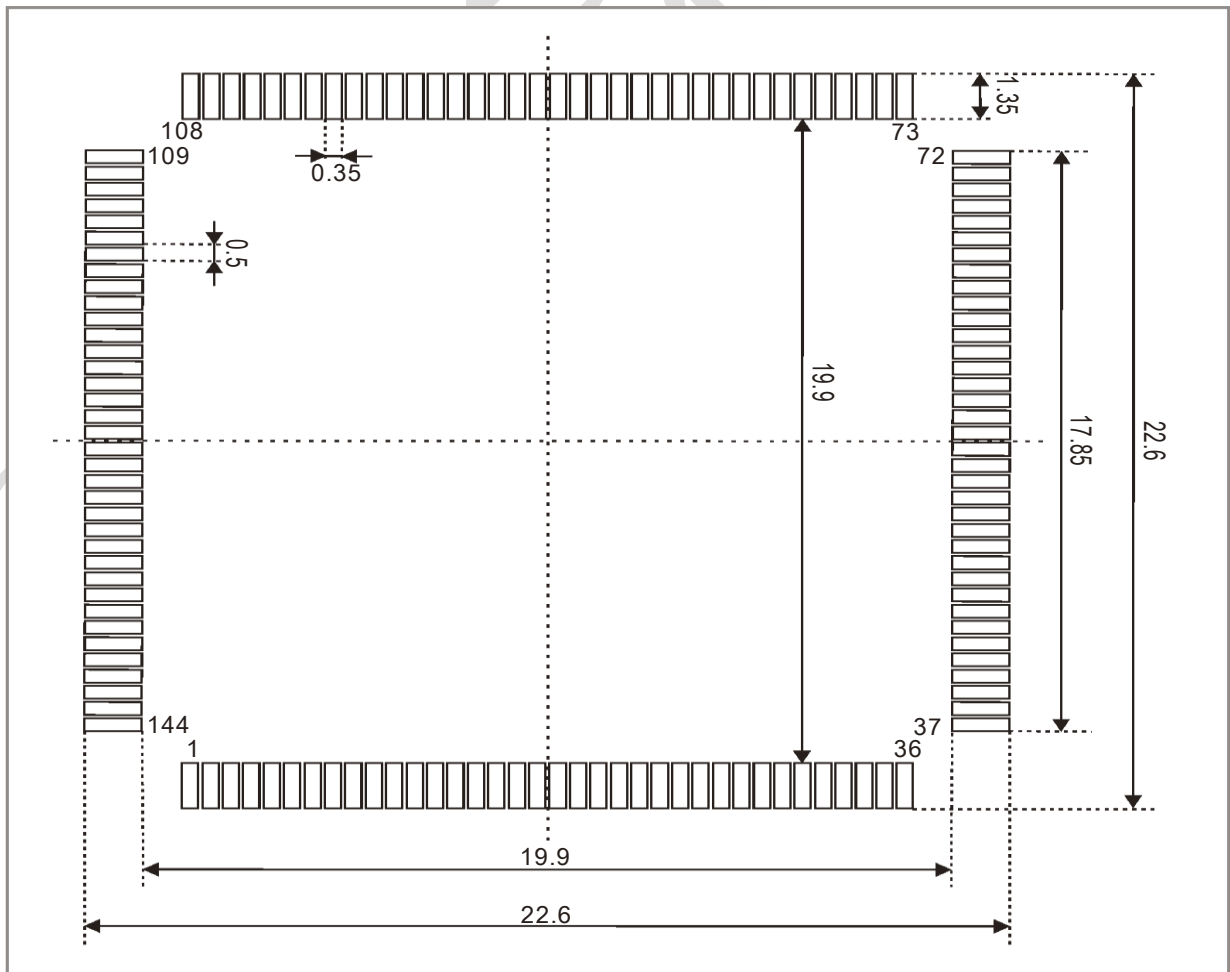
LQFP144 芯片的 PCB 安装尺寸图
